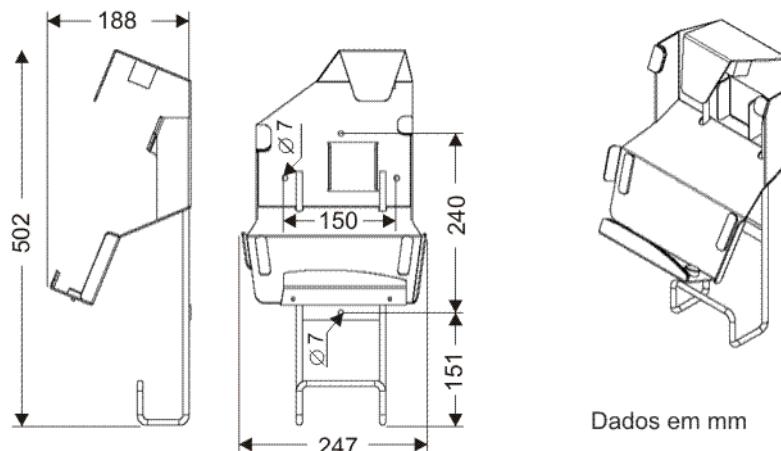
Dimensões e medidas de furos do suporte do smartPAD
